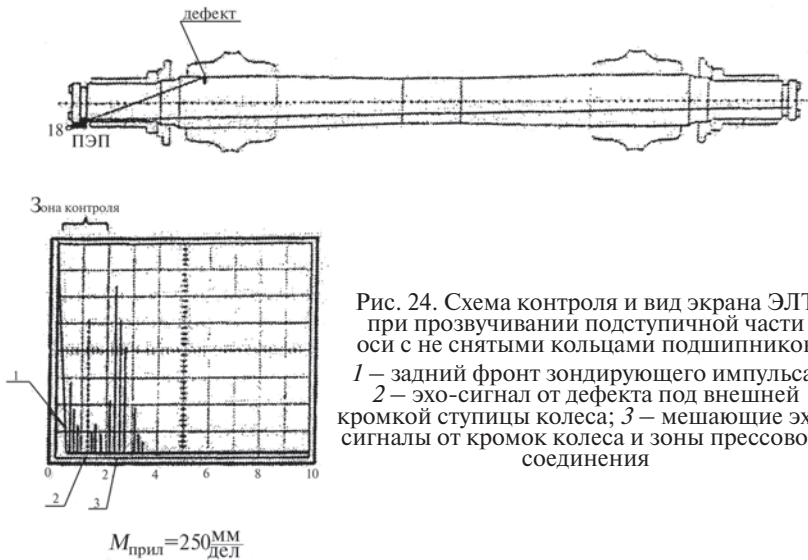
Схема контроля и вид экрана ЭЛТ при прозвучивании подступичной части оси с не снятыми кольцами подшипников
